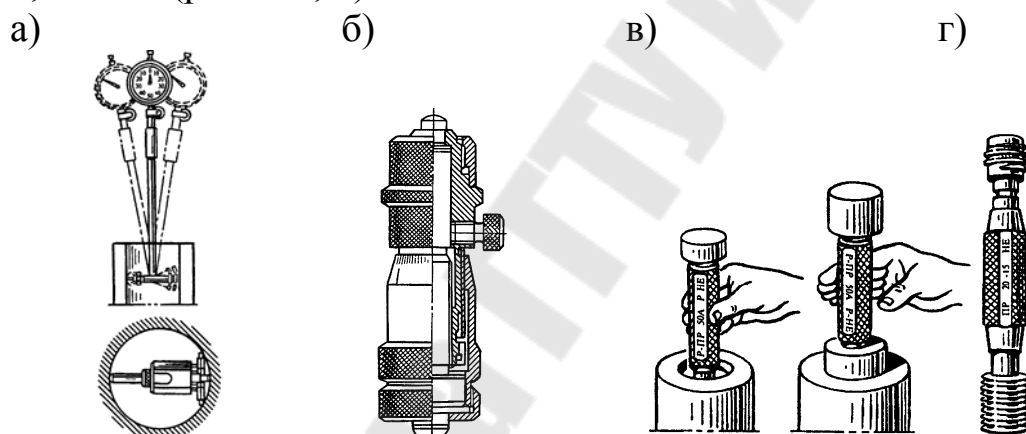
Контрольно-измерительные инструменты для отверстий:
